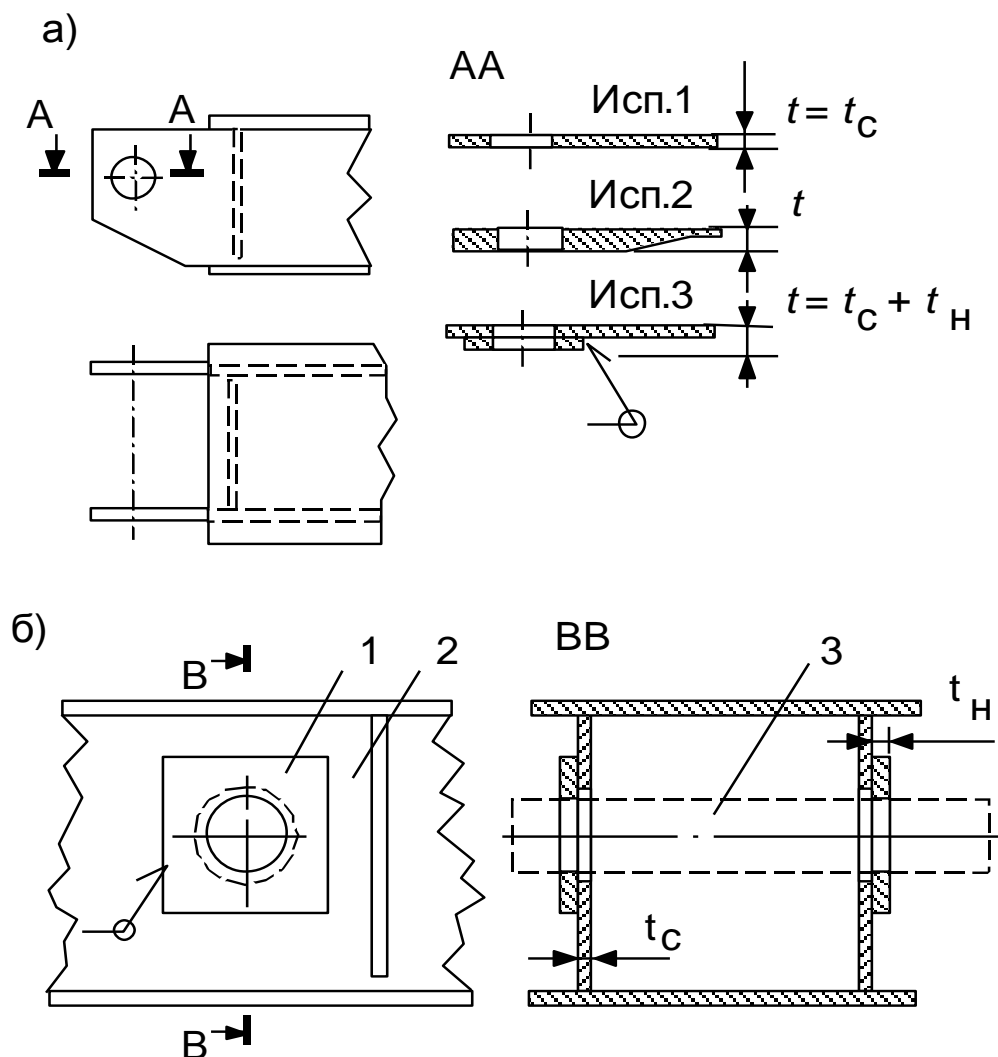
Схемы закрепления осей в листовой конструкции
